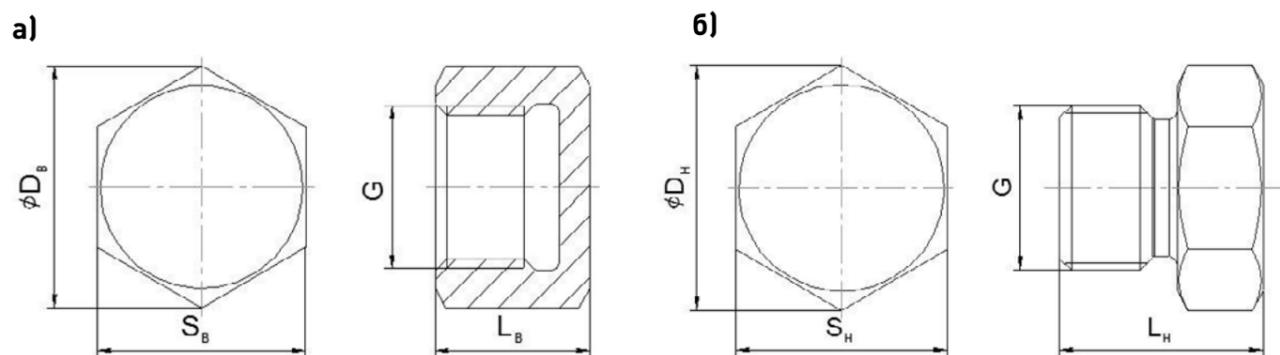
Заглушка испытательная: а) с внутренней резьбой; б) с наружной резьбой
